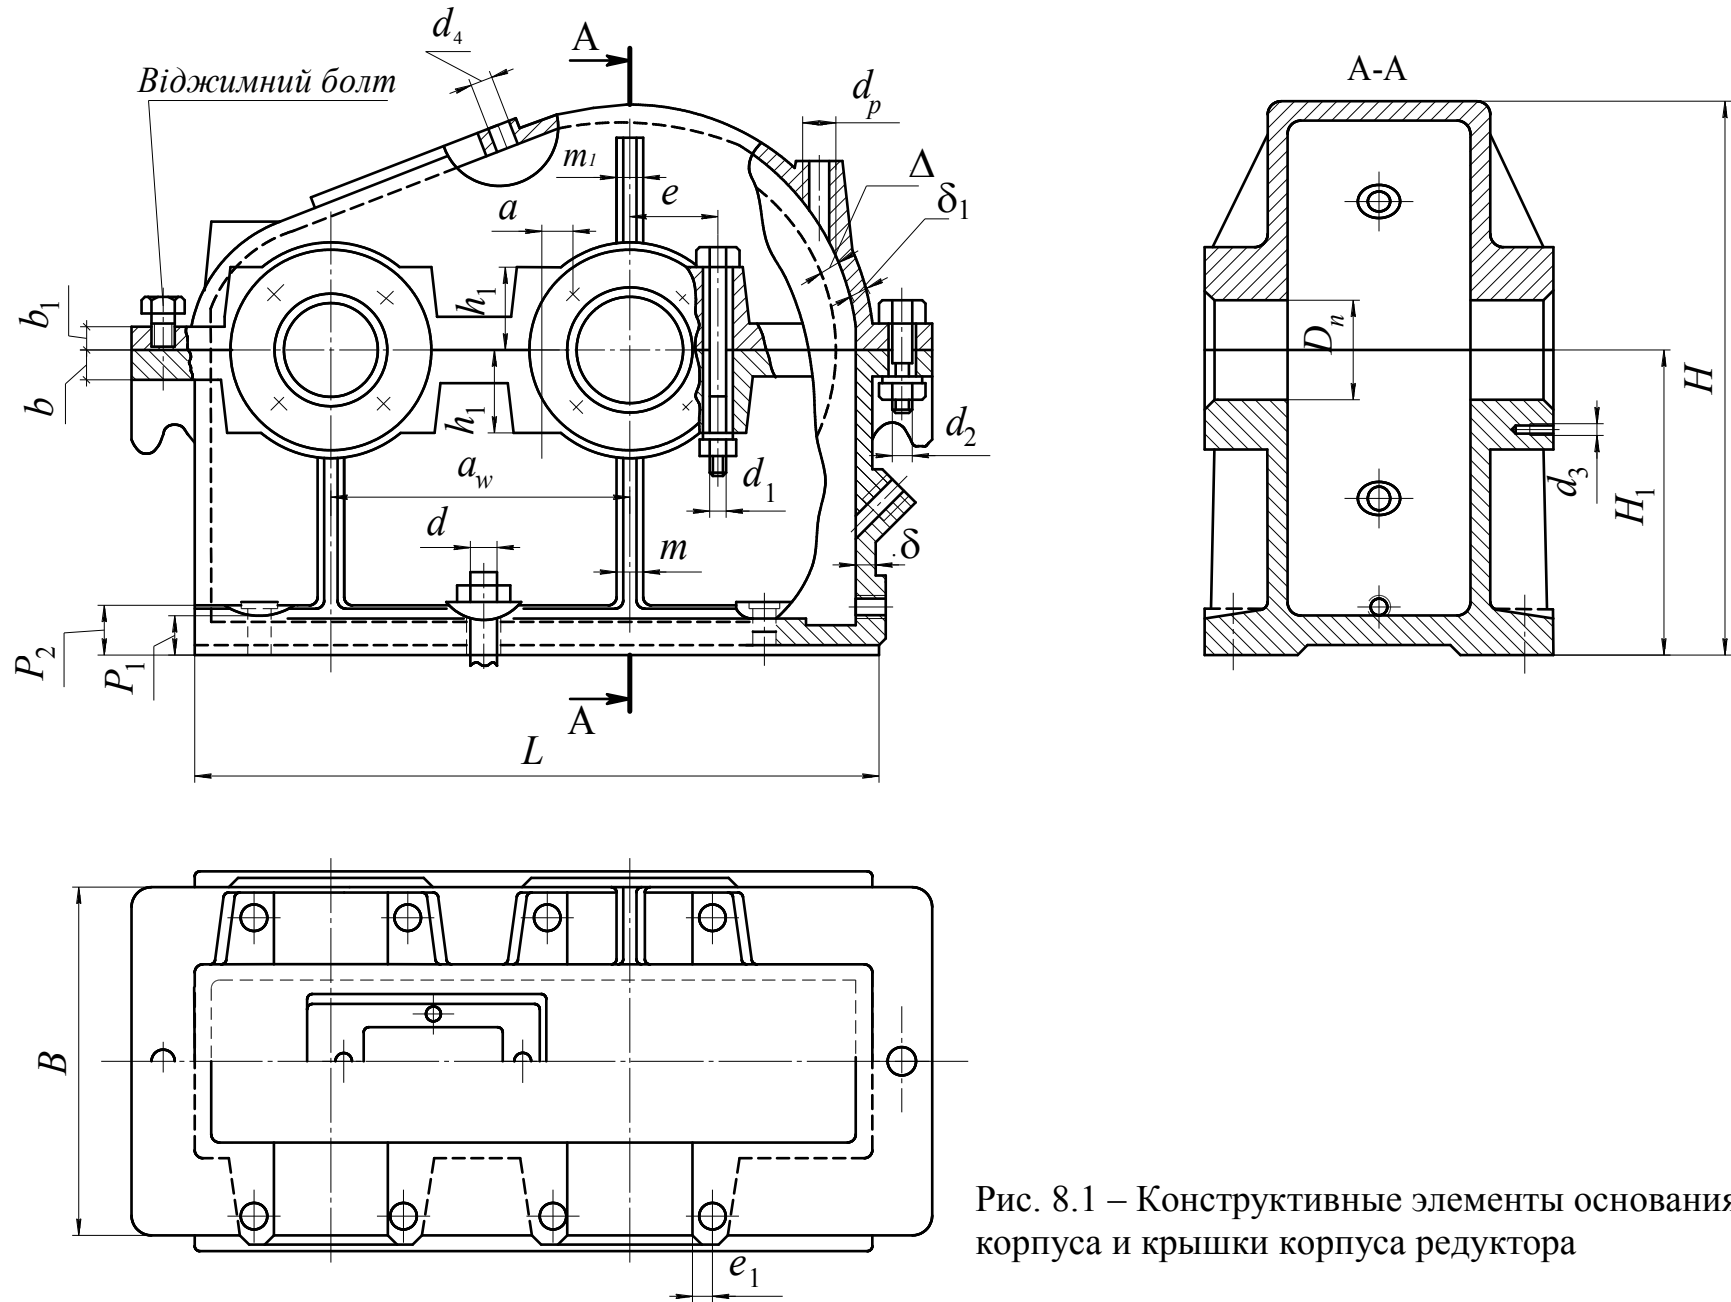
Конструктивные элементы основания корпуса и крышки корпуса редуктора
